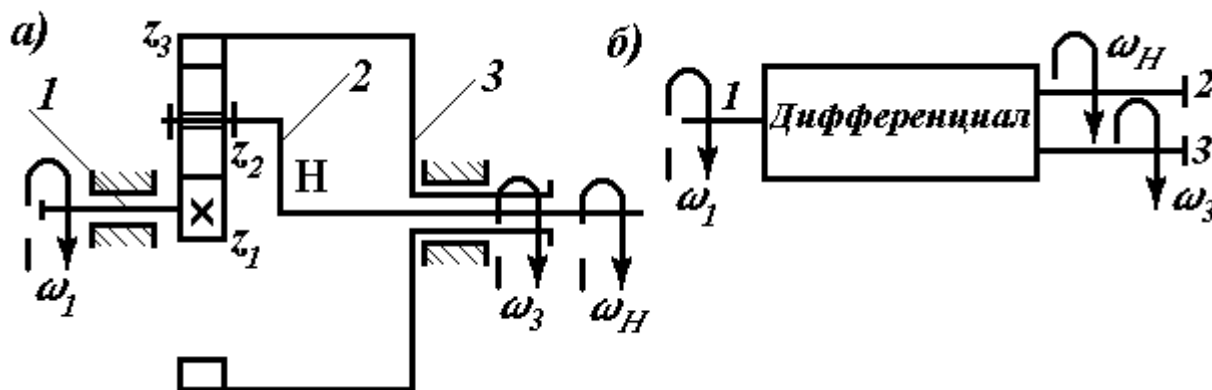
Дифференциальный механизм с цилиндрическими зубчатыми колесами:
